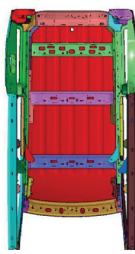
Dachaufbau mit Aufstelldach (Bild ABH)
